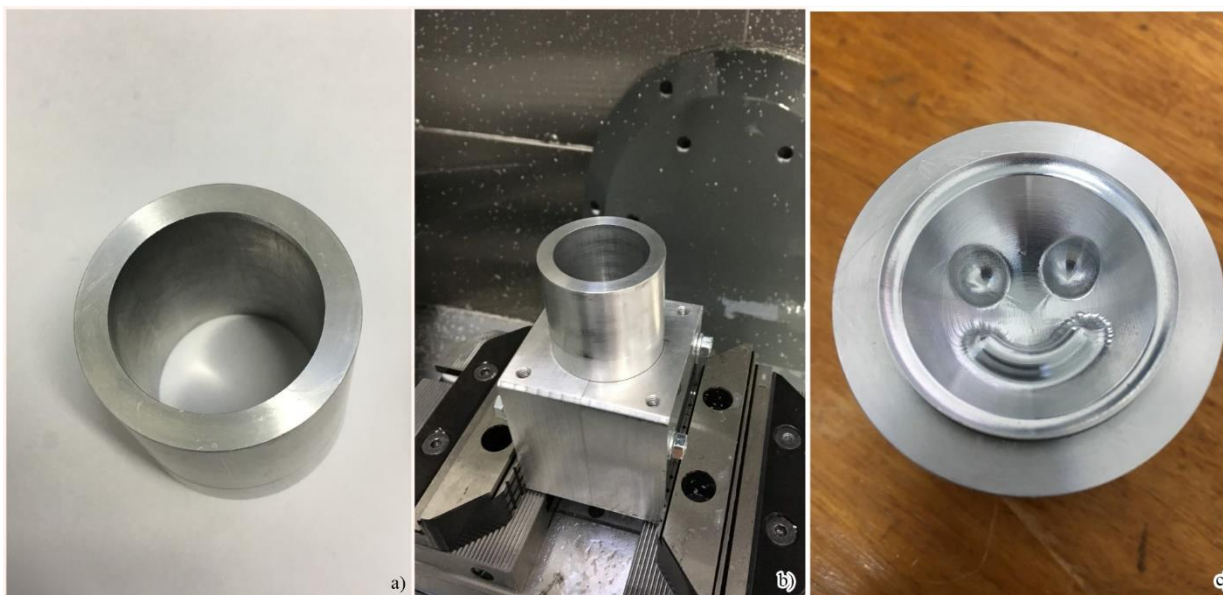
a) Casquilho fabricado; b) Montagem do casquilho sob duas partes laterais do molde; c) Êmbolo que faz a compactação do aglomerado e que se desloca no interior do casquilho
